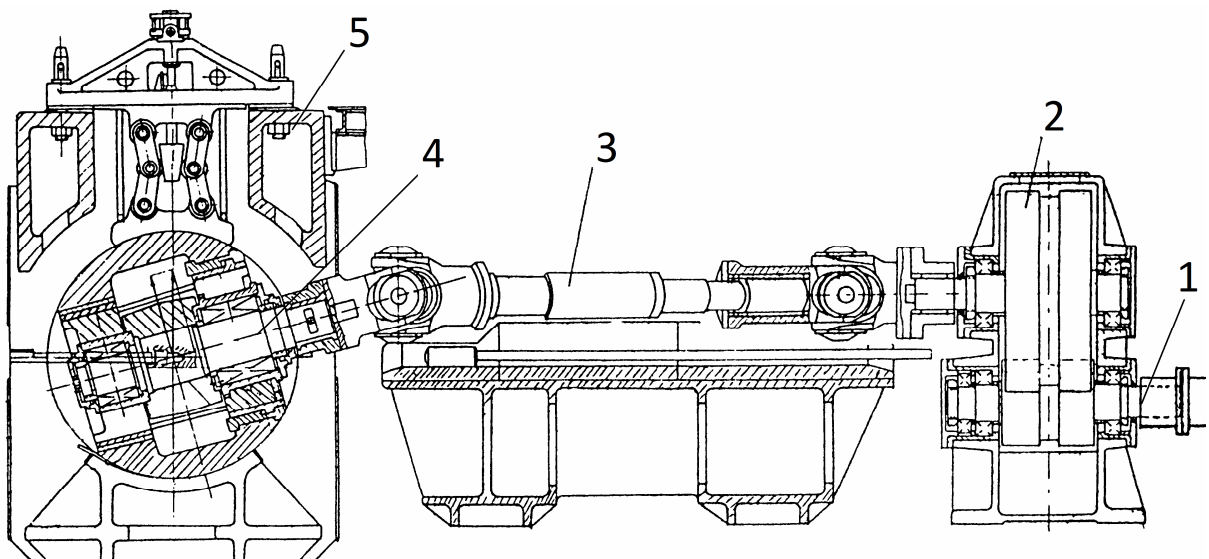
Привод валков рабочей клетки стана винтовой прокатки труб:
